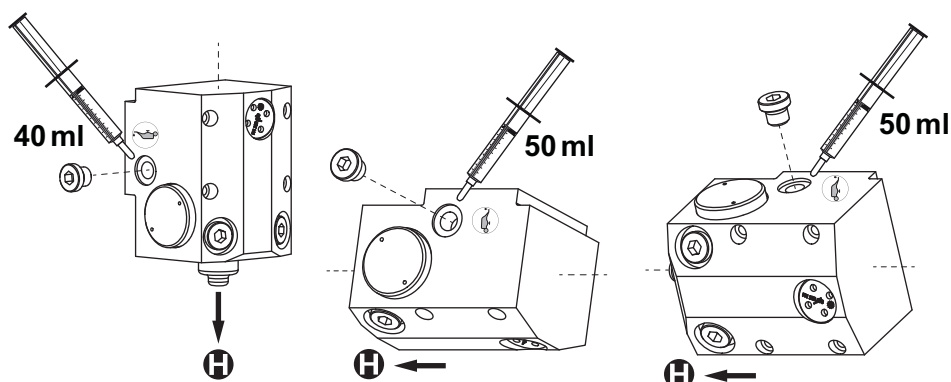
Remplissage en fluide d'exploitation pour HiPace 1800 versions « U » et « UC » dans les positions valables dans chaque cas
